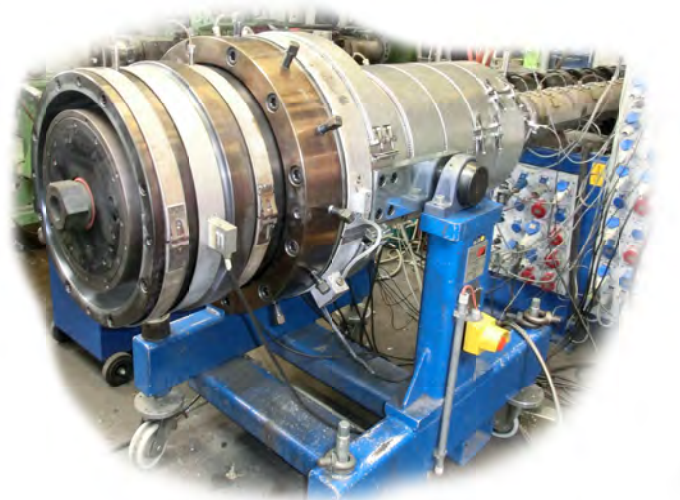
Extrusionswerkzeug RW-1-200/500 für dickwandige Rohre im praktischen Einsatz
